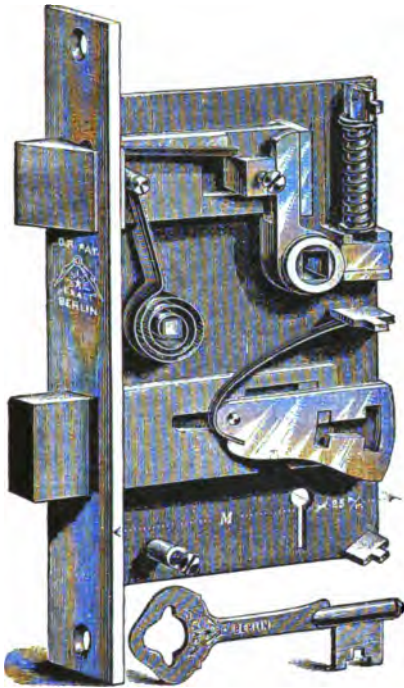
zeigt die Anwendung einer Chubb-Einrichtung bei einem gewöhnlichen Zimmerthürschloß mit schließender Falle ohne Nacht-
